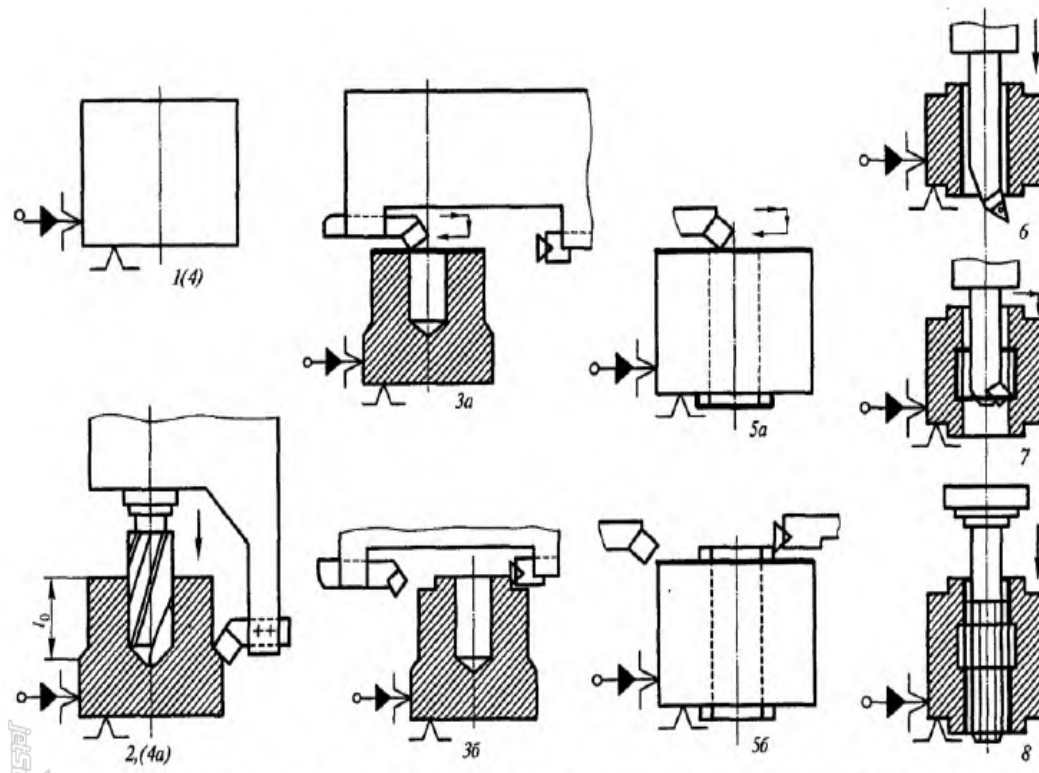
Схема оброблення червячної модульної фрези на 8-шпindelьному напівавтоматі моделі 1К82
